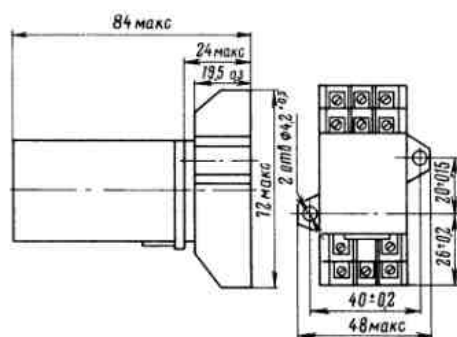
Габаритные и установочные размеры реле типов РПУ-О-911У4(Т4); РПУ-О-912У4(Т4); РПУ-О-961У4(Т4); РПУ-О-962У4(Т4)
